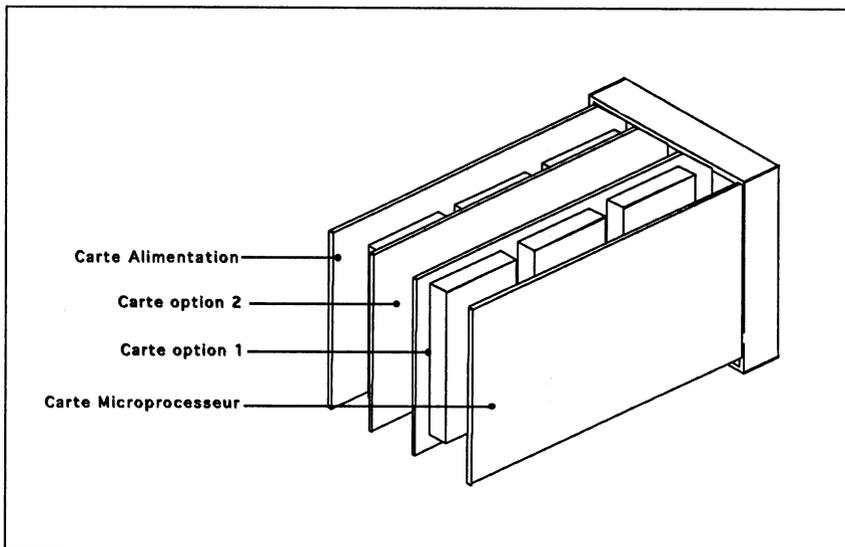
7 Emplacement des différentes cartes du régulateur 9000HP
